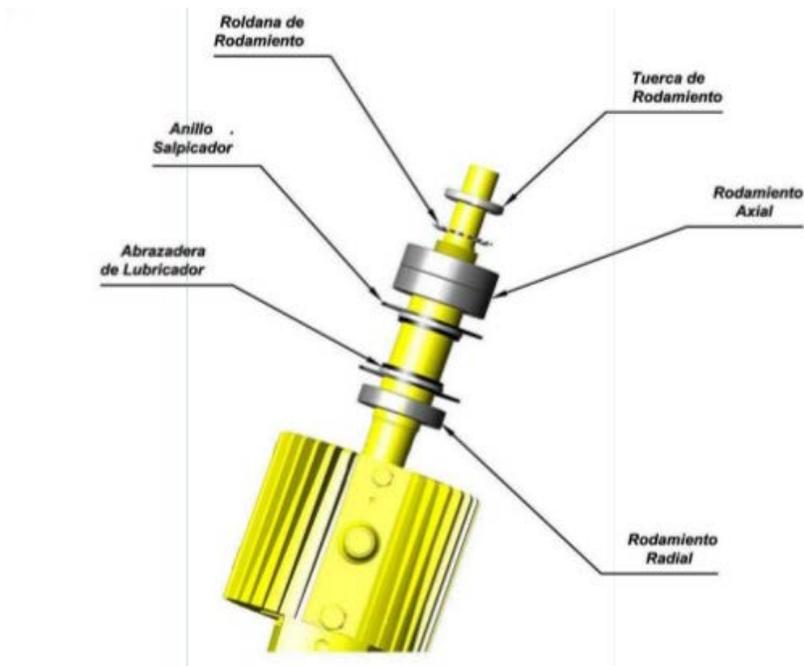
DESMONTAJE DE ANILLOS Y RODAMIENTOS
